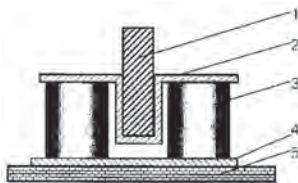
Конструктивная схема резинового виброизолятора обычного типа: 1–лапа станка; 2–S-образный кронштейн; 3–резиновый упругий элемент; 4–опорная поверхность; 5–межэтажное перекрытие.
